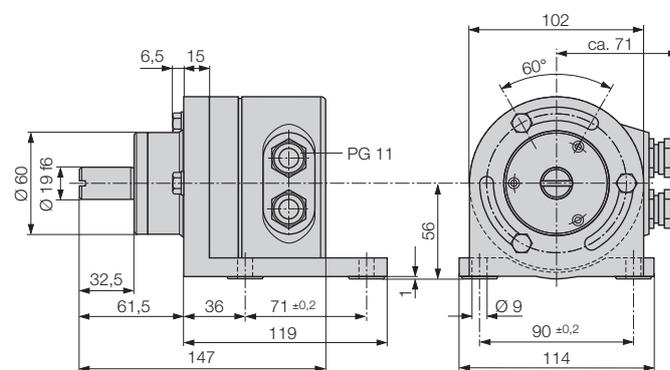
KINAX WT 707 avec bornes à vis, ainsi que presse-étoupes et pied.
